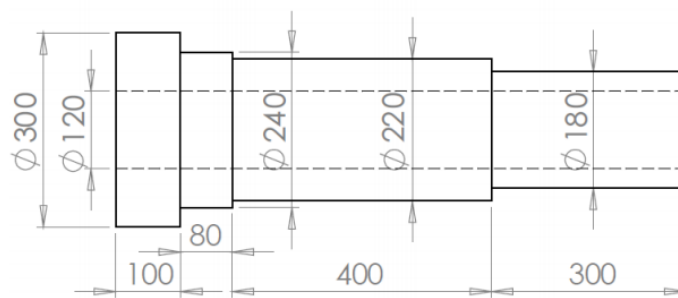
Detalhe das dimensões projetadas para a peça final forjada (GAO, 2013).
